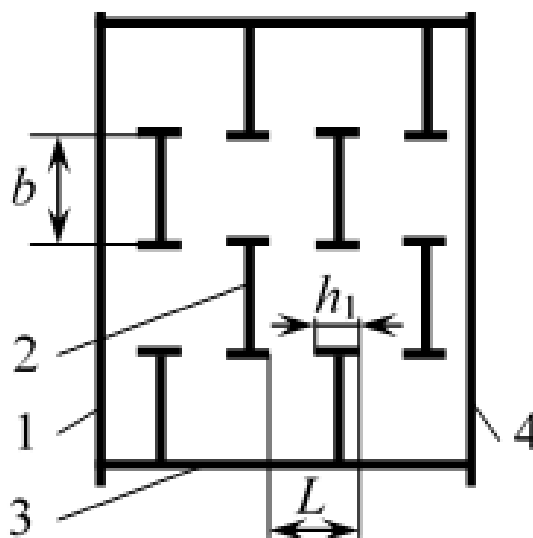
Упрощенная двухмерная модель сепаратора (вид сверху): 1 – входной патрубок; 2 – двутавровые элементы; 3 – корпус; 4 – выходной патрубок
